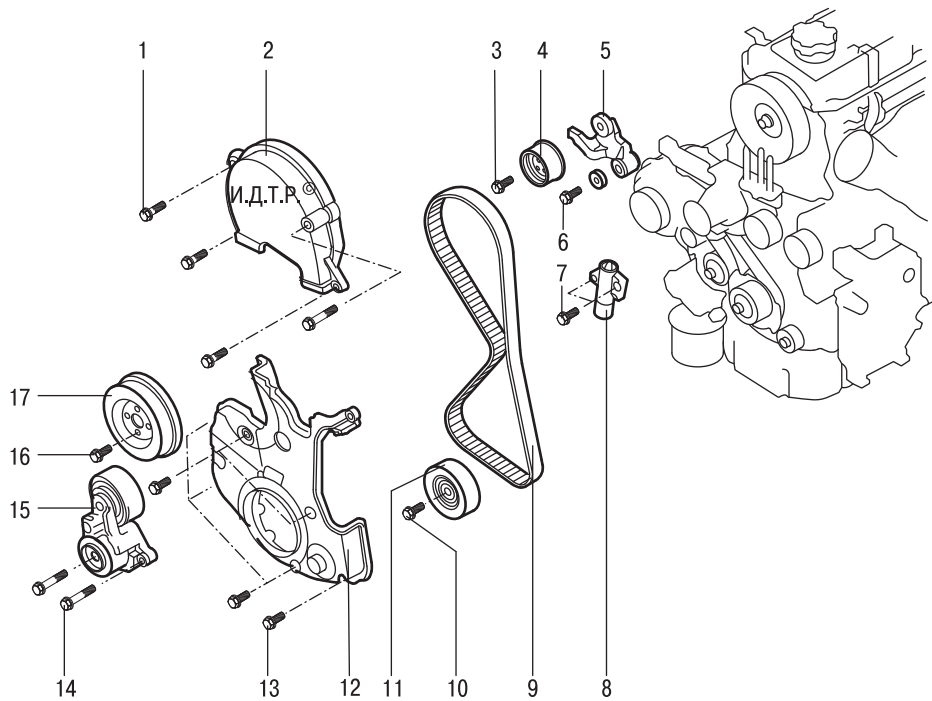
Привод газораспределительного механизма: 1 – болты крепления верхней крышки привода; 2 – крышка привода газораспределительного механизма; 3 – болт крепления натяжного ролика; 4 – натяжной ролик; 5 – рычаг автоматического натяжителя; 6 – болт оси рычага; 7 – болт крепления натяжителя; 8 – автоматический натяжитель; 9 – ремень привода газораспределительного механизма; 10 – болт крепления промежуточного ролика; 11 – промежуточный ролик; 12 – нижняя крышка привода; 13 – болты крепления нижней крышки привода; 14 – болты крепления автоматического натяжителя привода вспомогательных агрегатов; 15 – автоматический натяжитель привода вспомогательных агрегатов; 16 – болт крепления шкива; 17 – шкив водяного насоса
